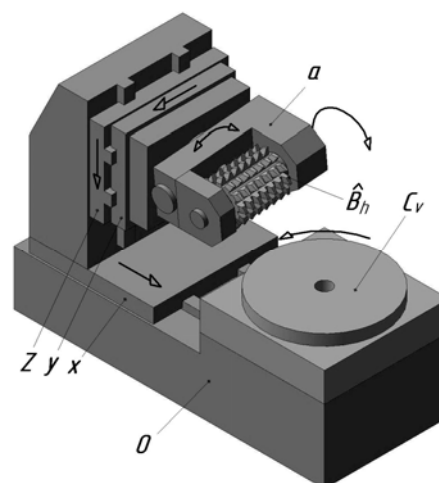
Компоновка зубофрезерного станка с формулой $COxZYa\hat{B}$
